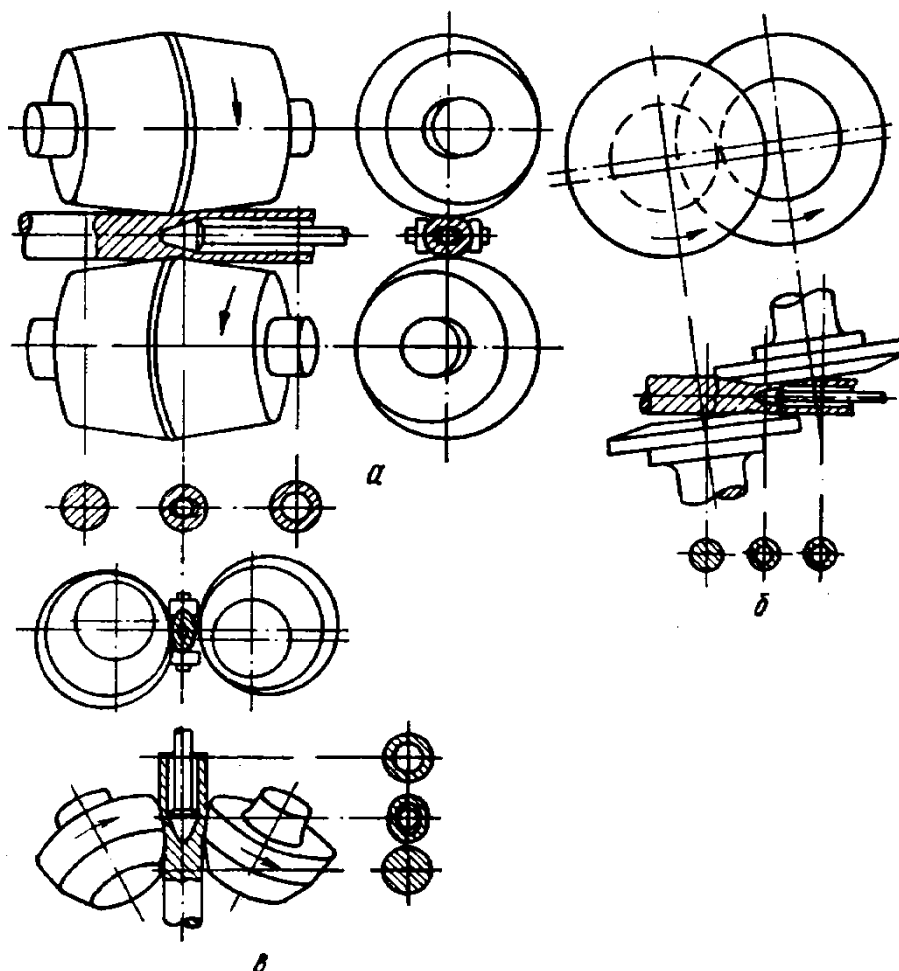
Схемы прошивки на двухвалковом стане поперечно-винтовой прокатки.(а-бочковидными валками, б-дисковыми валками, в-грибовидными валками)
